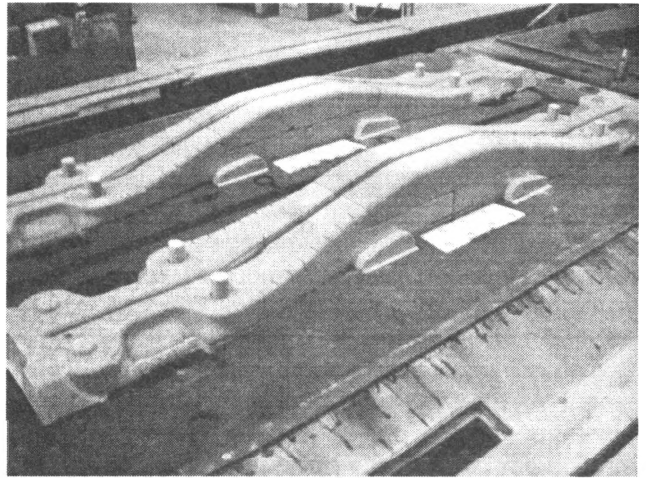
Полуформа низа с установленным комплектом стержней, изготовленных по «Alfa-set»- и «Cold-Box-amin»-технологиям отливки «балка надрессорная»
